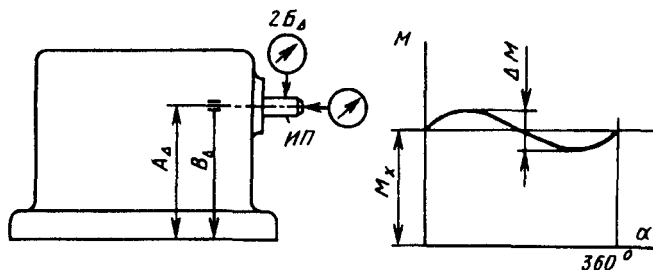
Требования к положению и движению выходного вала редуктора
